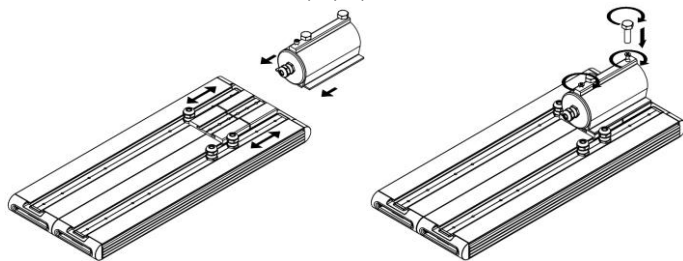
Установка крепления на соединительные планки на примере светильника Element 0,5x2 и Крепления Консоль без регулировки.
